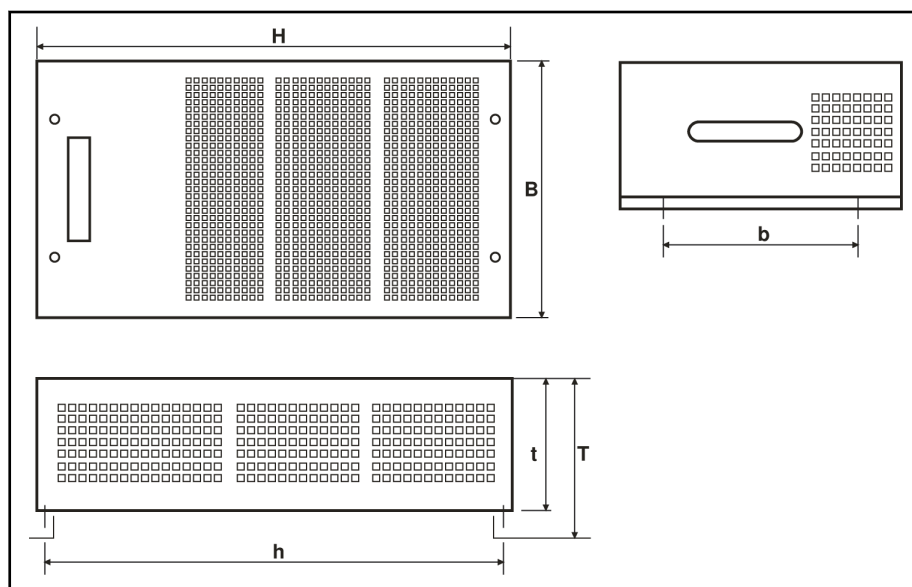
Чертеж размеров кожуха тормозного резистора
